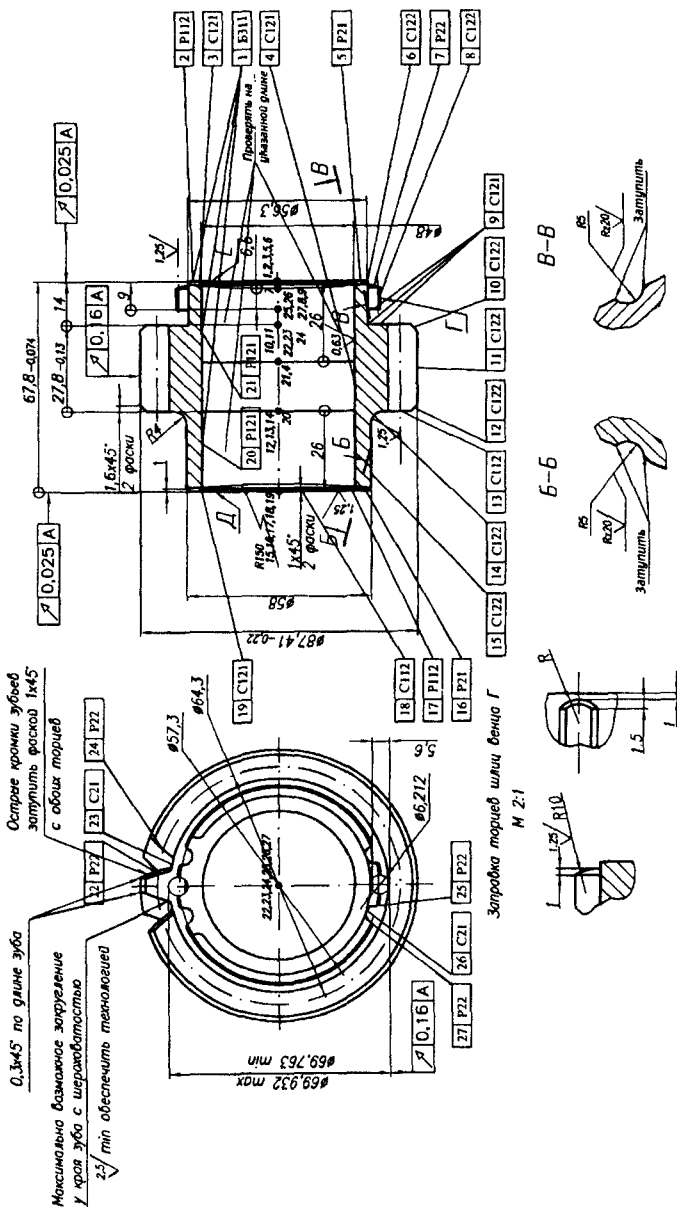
Чертеж шестерни вала коробки отбора мощности в модульном исполнении
